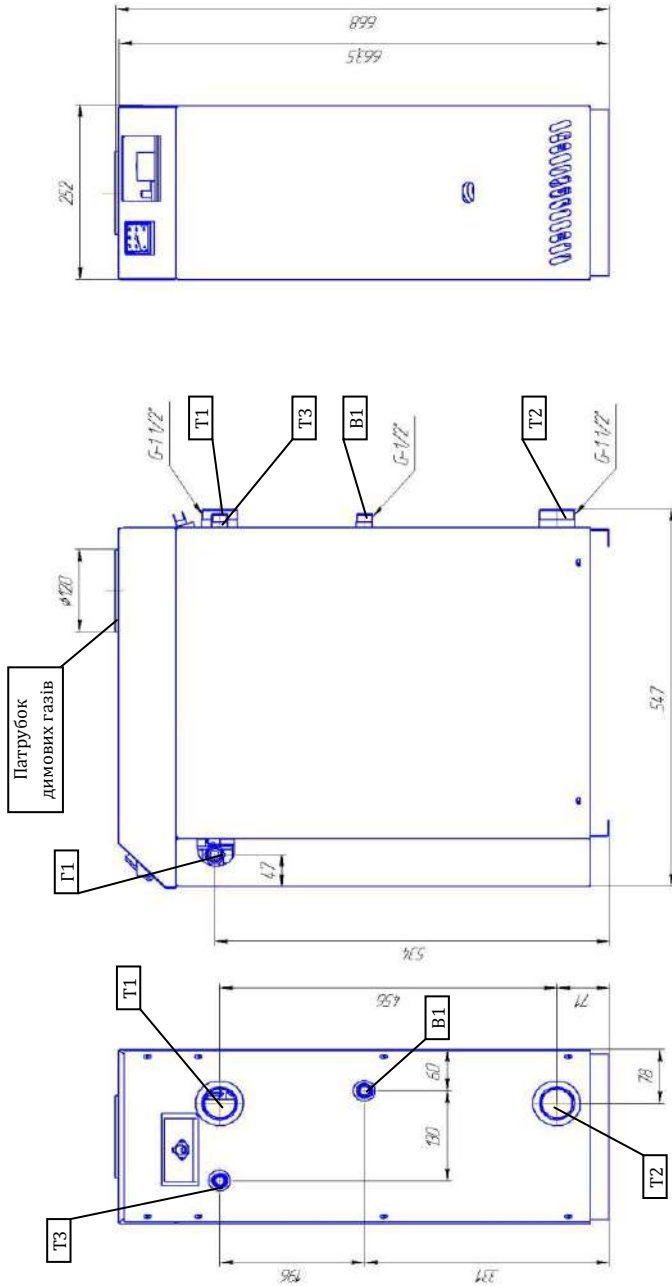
Установчі креслення апаратів КТ 8 TS (П2) Л,М ; «СТАНДАРТ»
